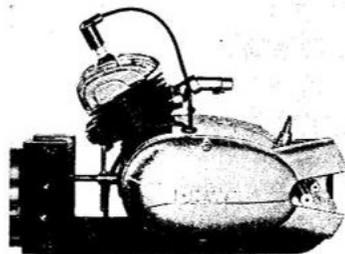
Motor kpl. am Aufnahmearm im Universal-Montagebock festgespannt
